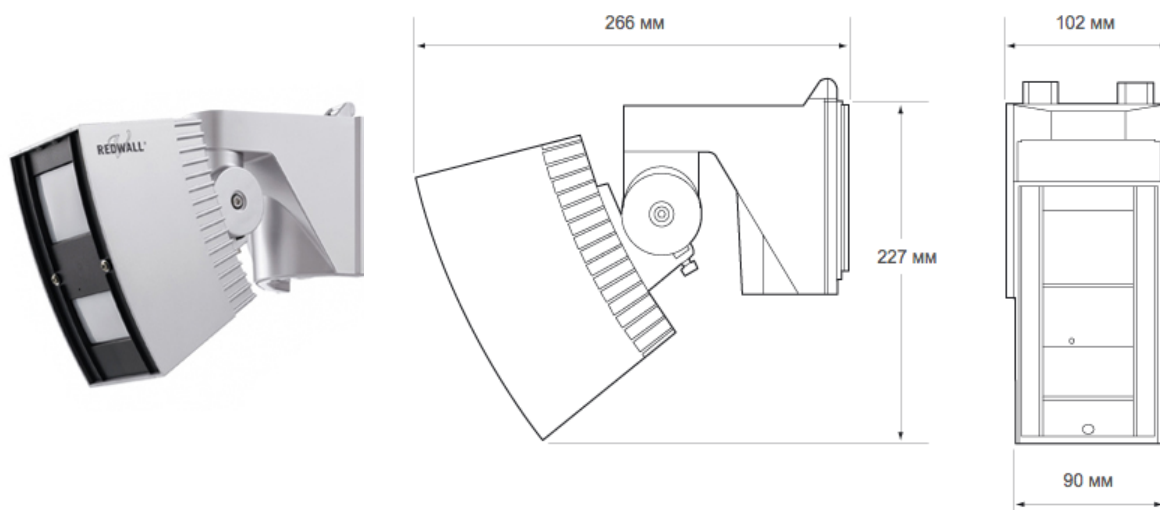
Общий вид и размеры ИК-извещателя Optex SIP-404
